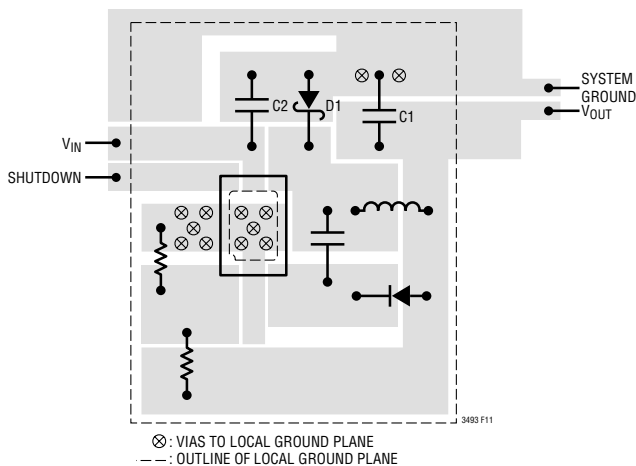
：上佳的 PCB 布局保证了正确的低 EMI 操作
